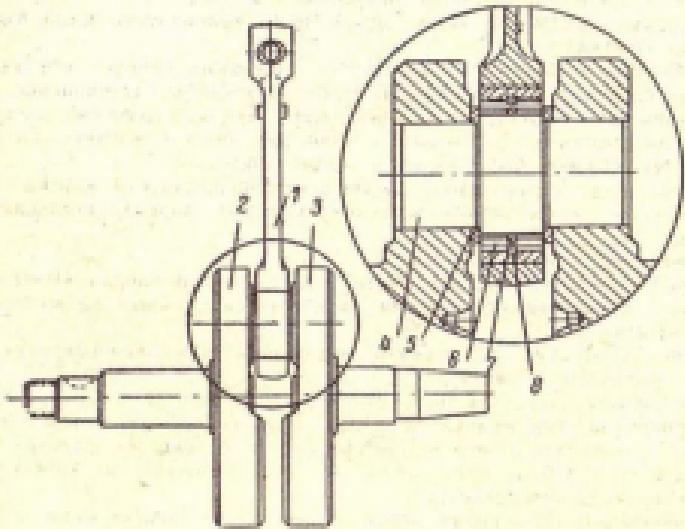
Сборка коленчатого вала мотороллера „Тула“:
